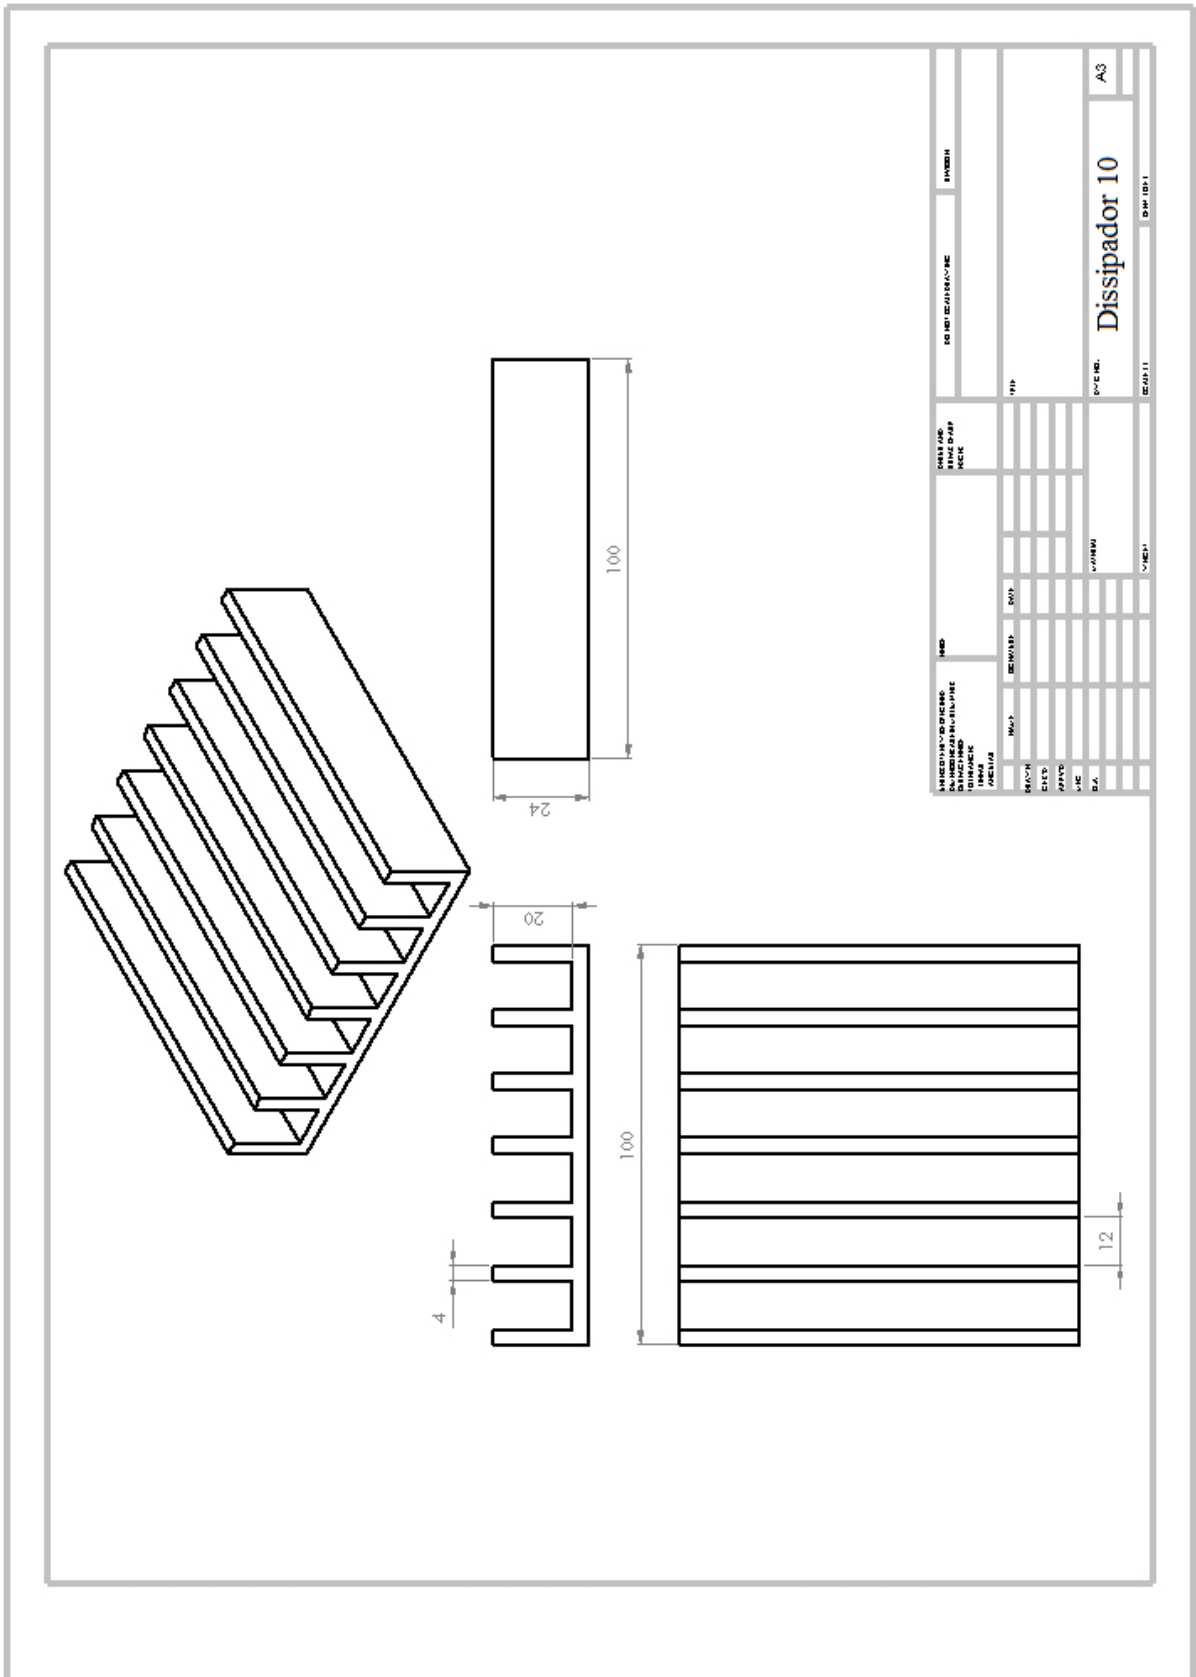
Desenho técnico utilizado para confecção do Dissipador 10.
